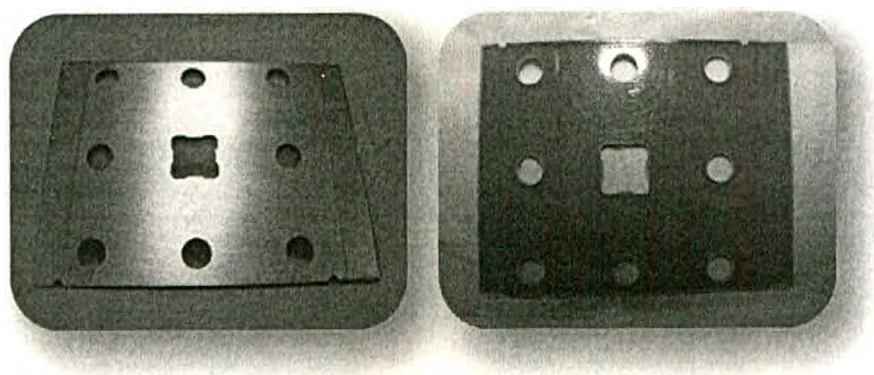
Placa de PCB mecanizada con ventana para la visualización de la placa difusora. Izquierda: cara en contacto con el carbón. Derecha: cara exterior de la celda donde se conectan los tubos para la entrada y salida del metanol.
